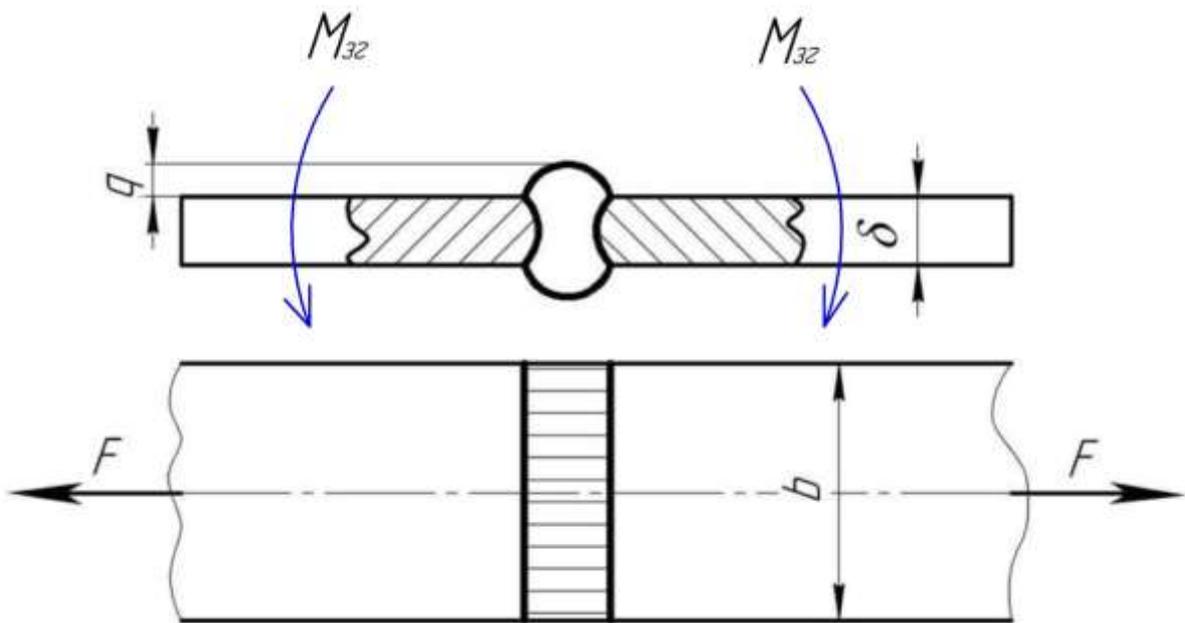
Розрахункова схема зварного з'єднання стиковим швом
